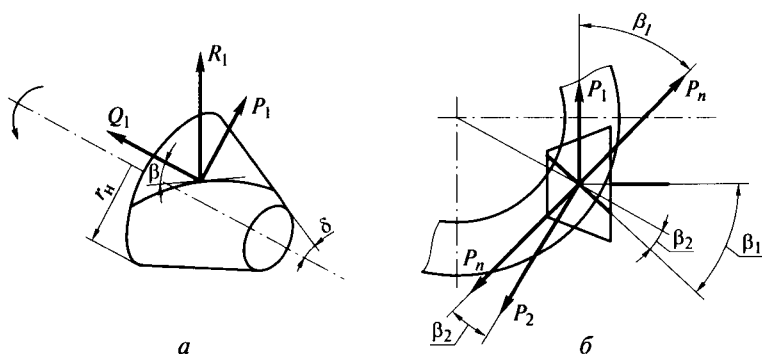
Схема сил для ведущей конической шестерни (а) и для гипоидной пары (б):
